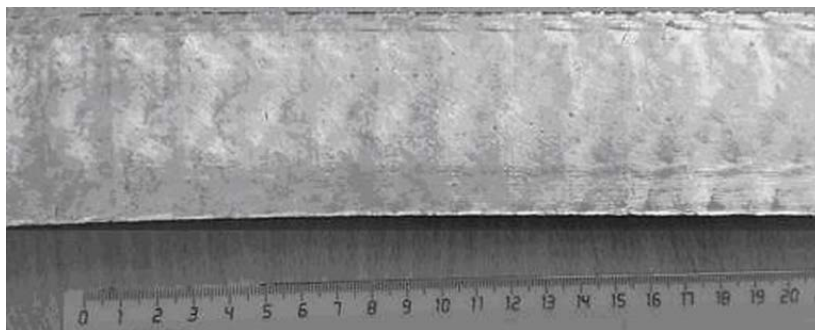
Внешний вид плоской заготовки из сплава Д1
